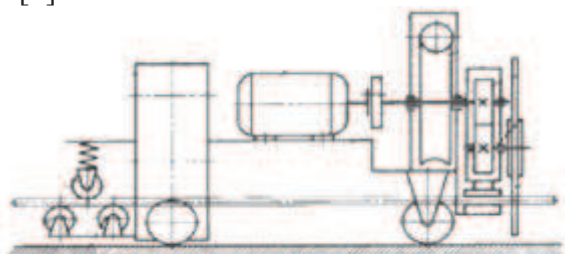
Устройство для движущихся профилей, вид сбоку
